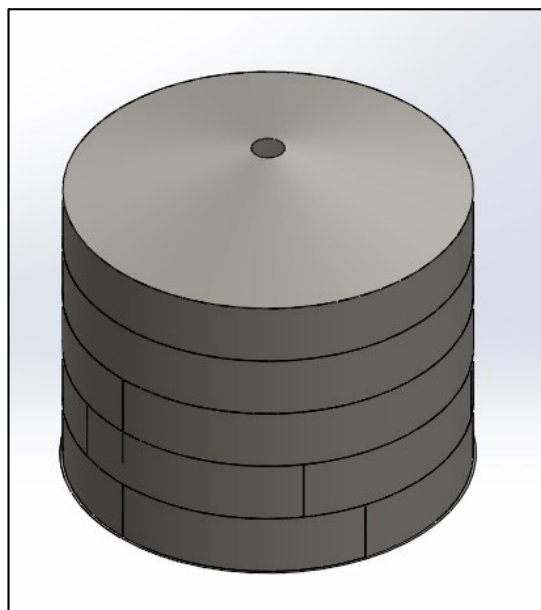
, Diseño de tanque de 600 m3 en solidworks.
